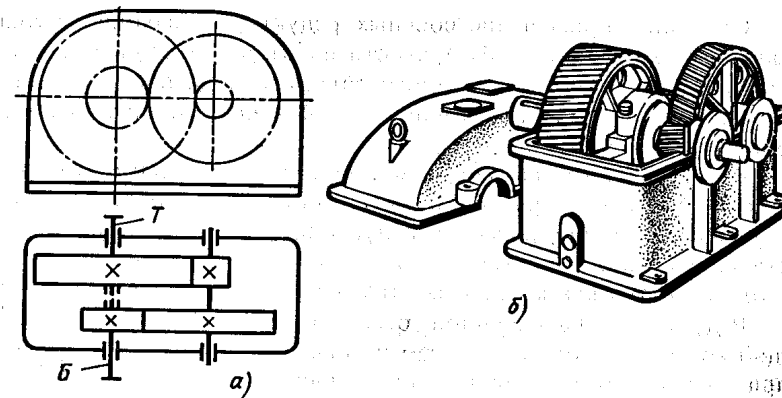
Двухступенчатый горизонтальный соосный редуктор: а — кинематическая схема; б — общий вид
